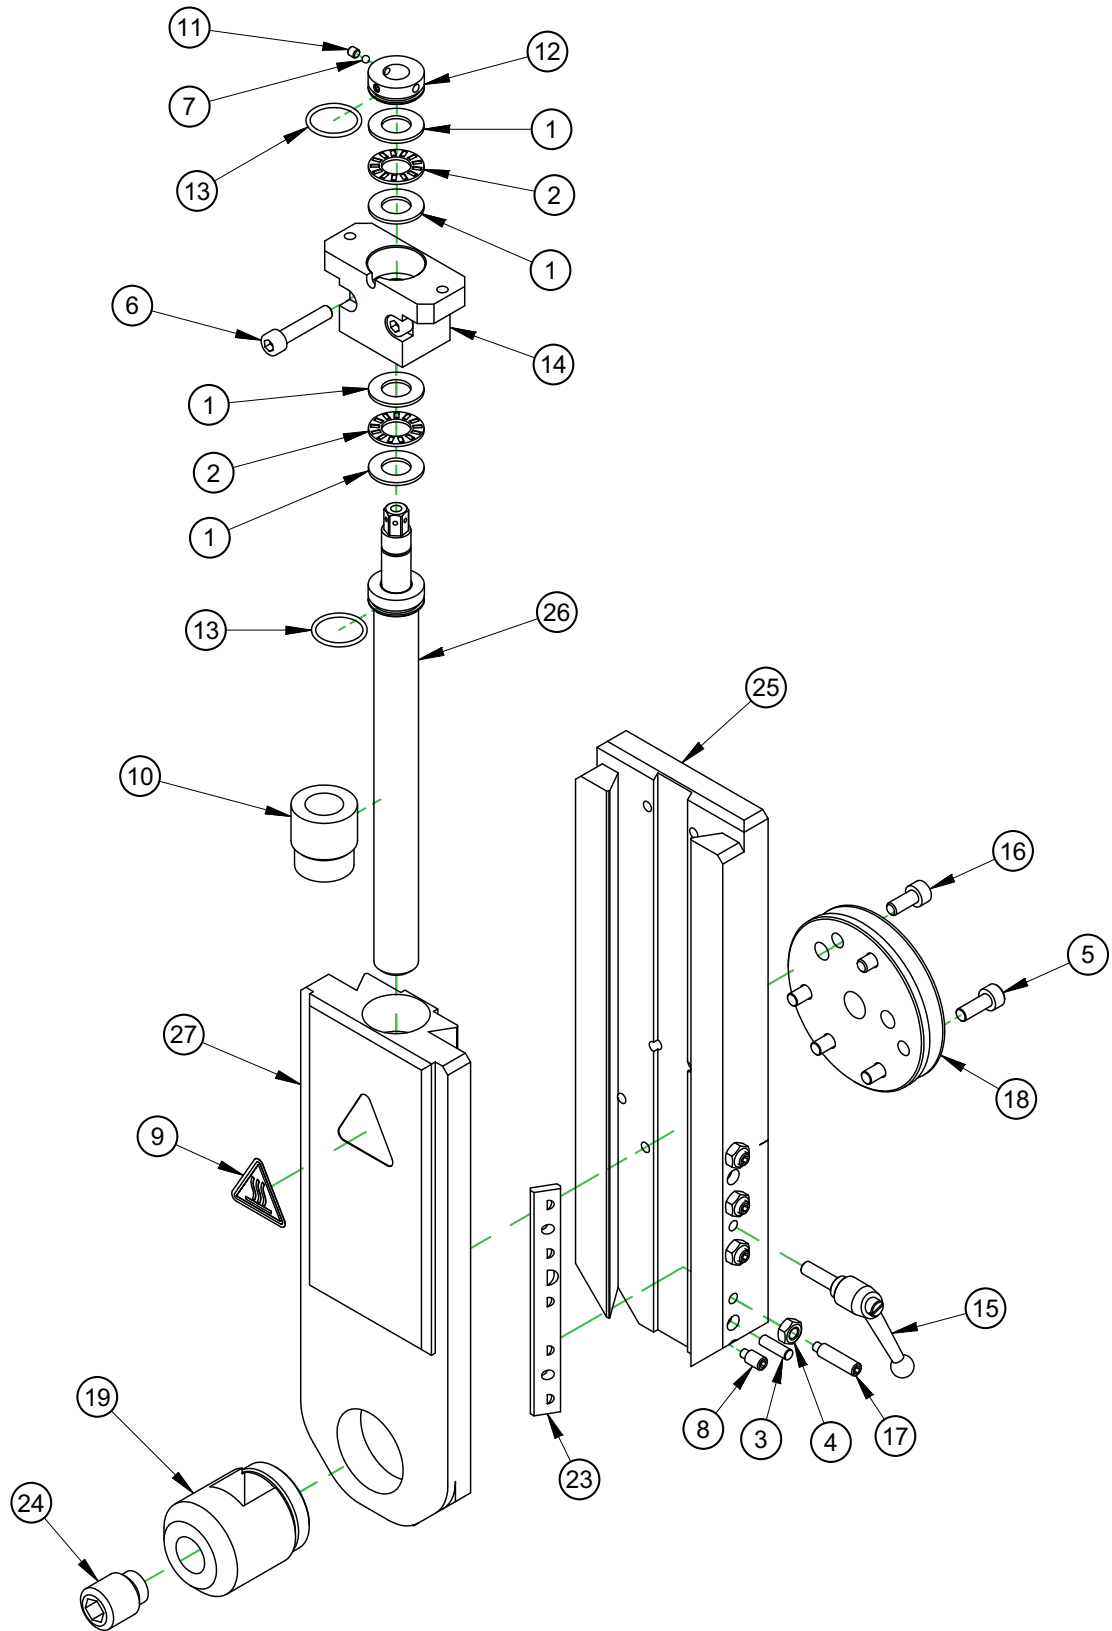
CONJUNTO DE PORTAHERRAMIENTAS DE DESLIZAMIENTO (N/P 89210)
